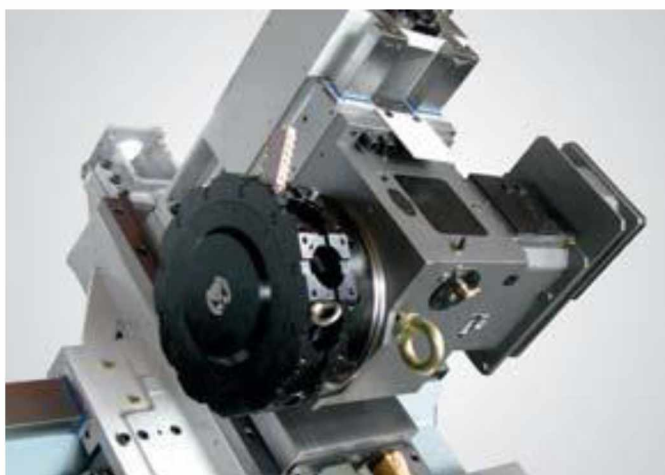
Револьверна головка верстат з ЧПК моделі CHALLENGER 117HT
